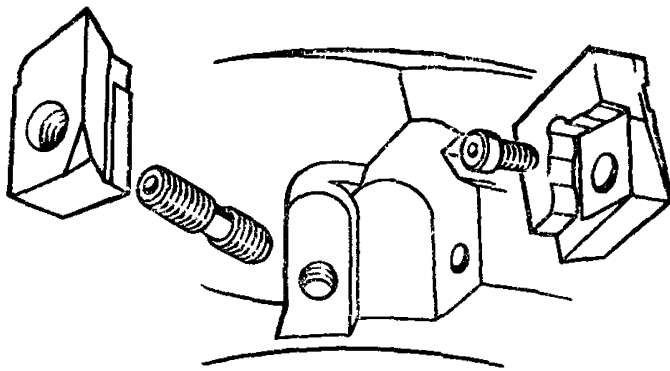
Пример унифицированного конструктивного решения установки съемного гнезда для закрепления пластины в модульной фрезе
